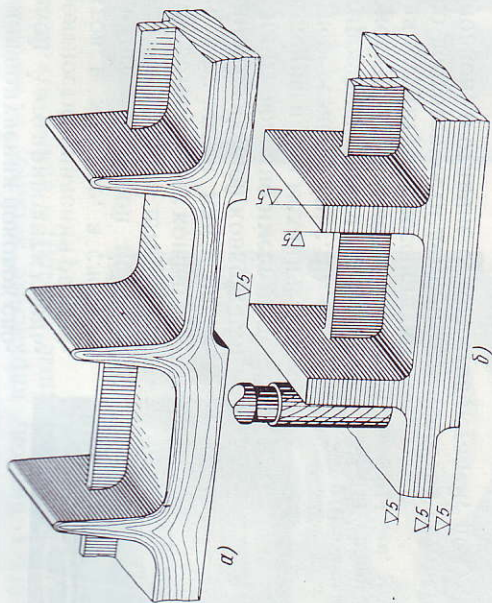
Схема расположения волокон в штампованных поковках (а) и обрабатываемых резанием деталях из катаных и кованых заготовок (б)
